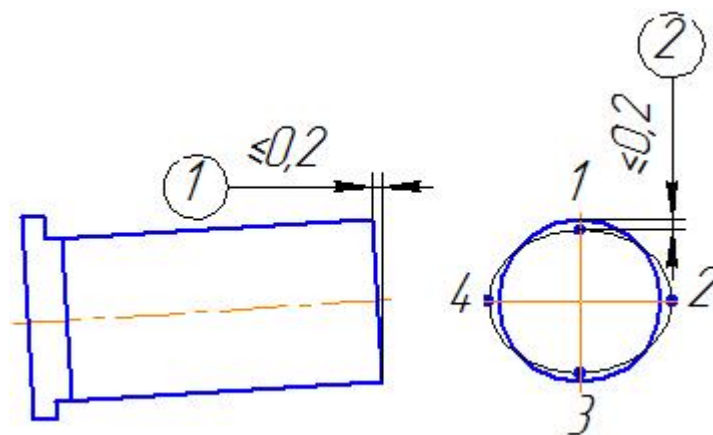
Контролируемые параметры при установке технологического узла №2 для сварки изнутри
